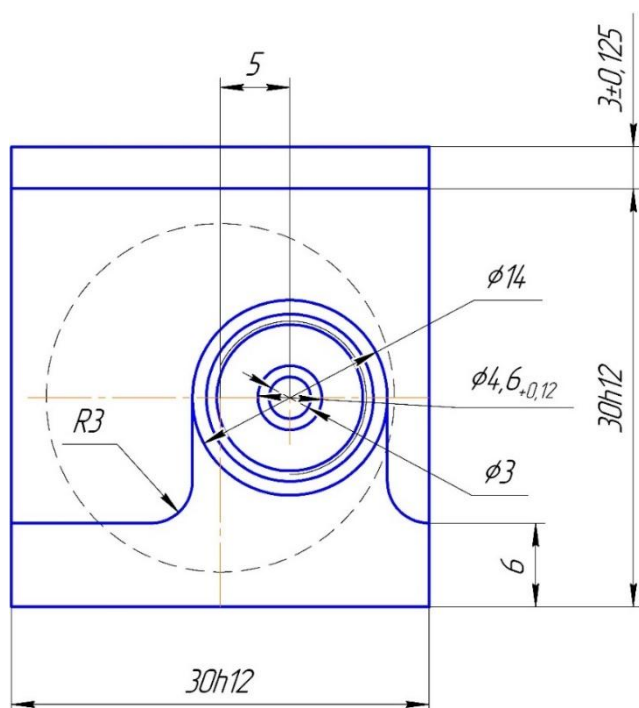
Деталь «Корпус влагопоглатителя»
